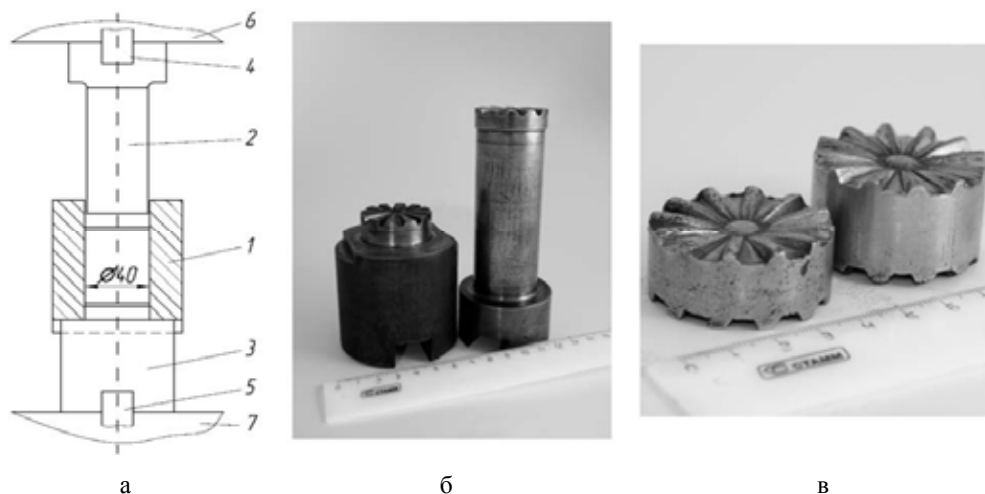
Схема устройства (а), внешний вид пуансонов (б) и образцы прессовок (в) при реализации схемы сжатия с кручением брикетов из стружки
